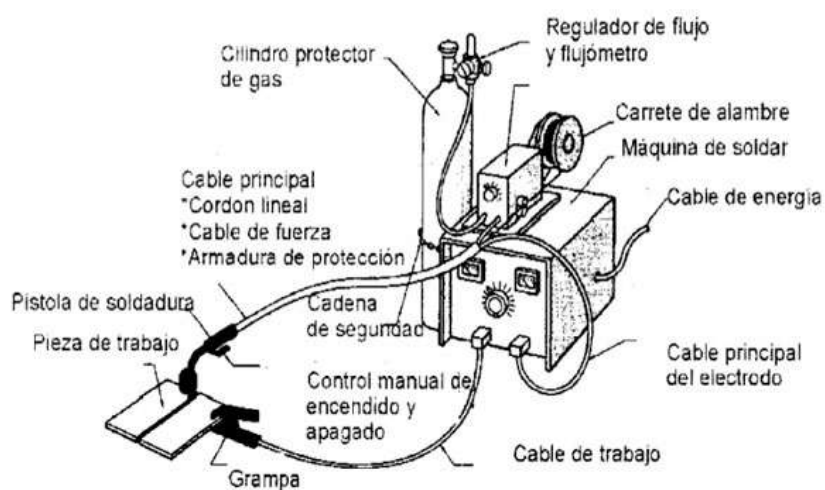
esquema de soldadura MIG/MAG, fuente: "RSF Maquinaria (blog)"
